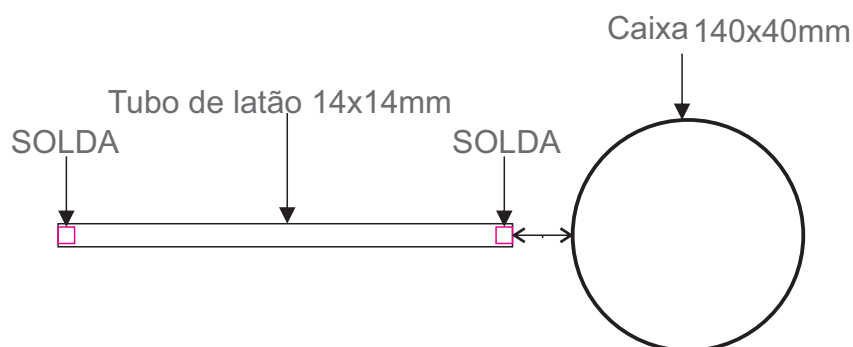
Esquema de fabrico da parte 3, produto 1.
